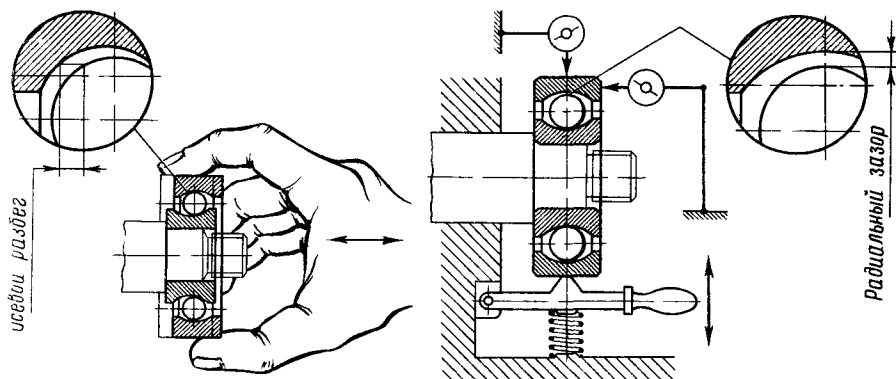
Приспособление для измерения зазора в подшипниках качения
